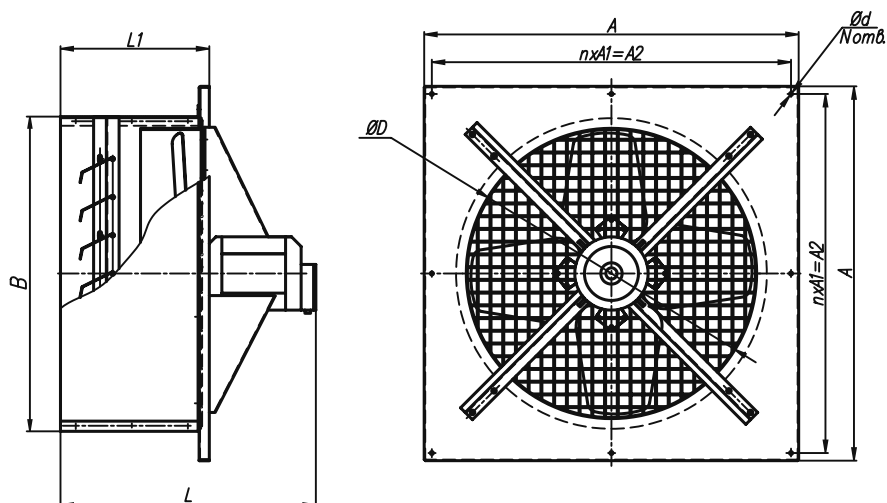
Габаритные размеры вентиляторов ВО №2,5-8 380 В.
